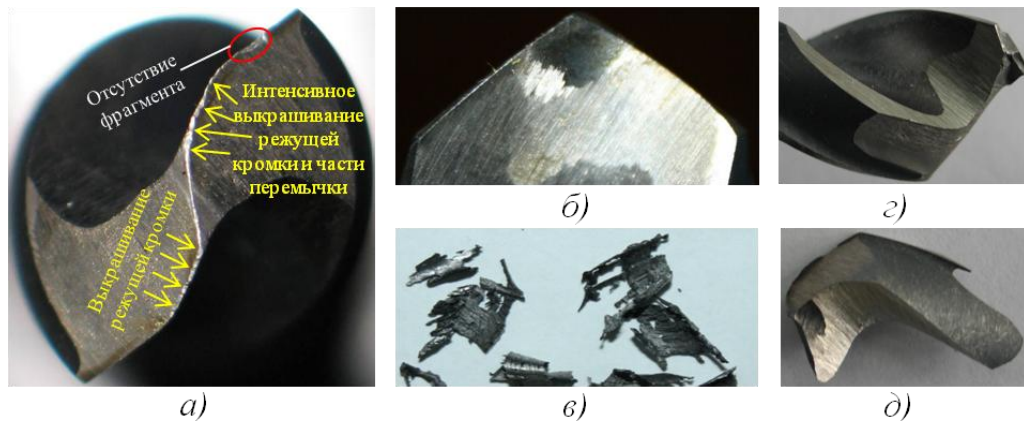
Состояние режущей части спирального сверла после сверления на втором режиме $n_2 = 200 \text{ мин}^{-1}$, $S_2 = 0,05 \text{ мм/об}$: 3 заготовок / 12 минут (а – задняя поверхность, б – передняя поверхность, в – форма образующейся стружки во время сверления); 6 заготовок / 24 минут (г, д – разрушение режущей части спирального сверла).
